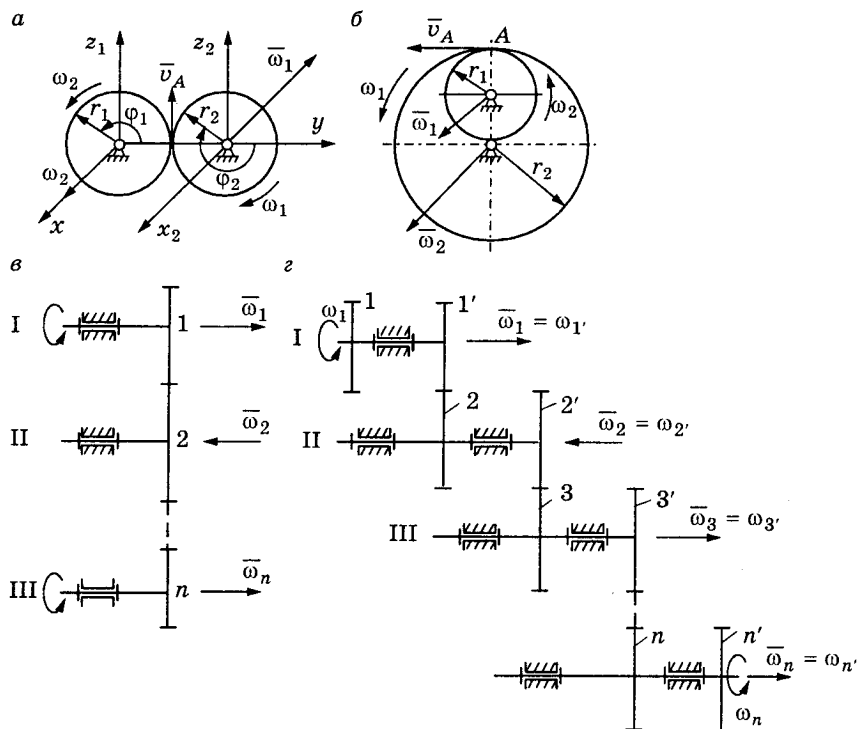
Схемы зубчатых передач с круглыми колесами:
